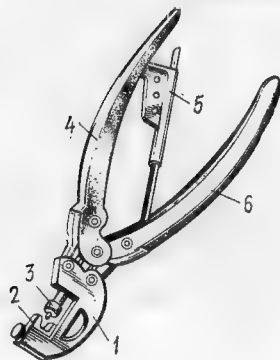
1 — головка; 2 — матрица; 3 — пуансон; 4 — рычаг подвижный; 5 — устройство блокирующее; 6 — рычаг неподвижный
